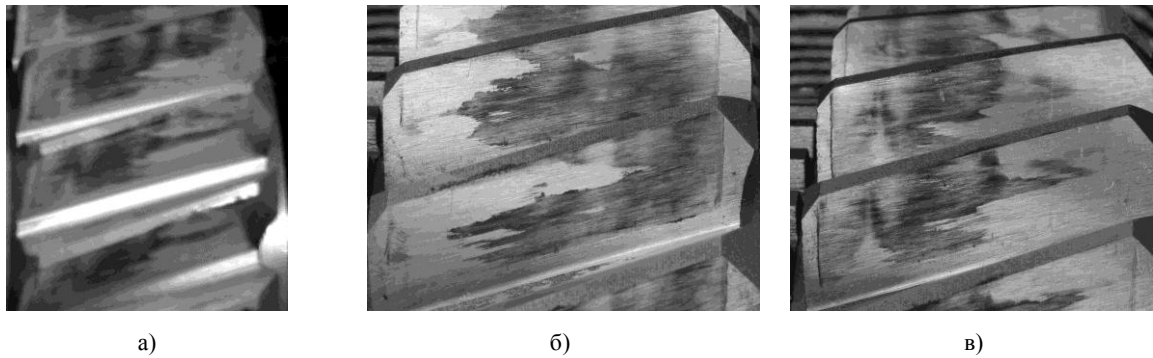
Дефекты пятна касания производственных зубчатых колес после зубошлифования: а – кромочный контакт; б – разрыв пятна касания по высоте; в – разрыв пятна касания по длине
